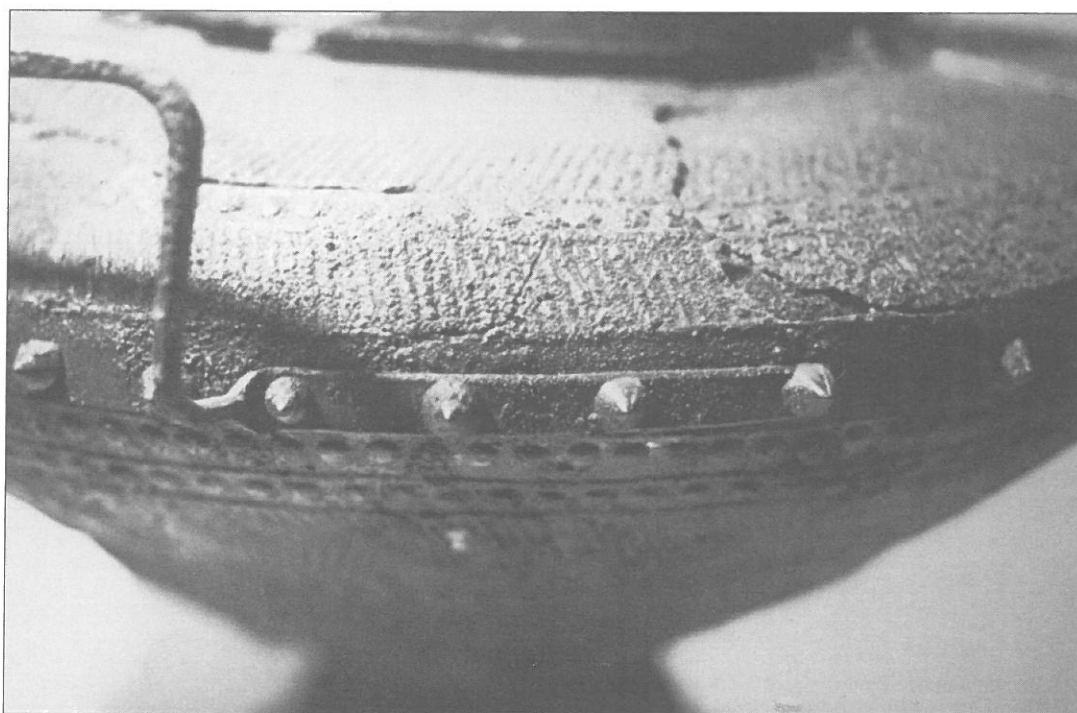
Rivets à tête conique utilisés pour l'assemblage par rivetage de deux tôles d'une urne métallique de la nécropole de Monterozzi, Tarquinia.
